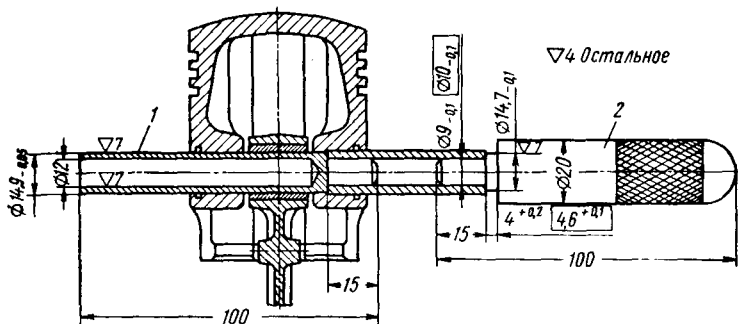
Приспособление для установки поршневого пальца (размеры для мотороллеров ВП-150 и В-150М даны в рамках):
